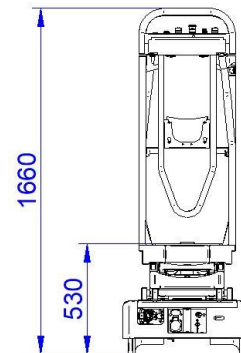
; Dimensions de la hauteur minimale en mm, 2 pantographes
